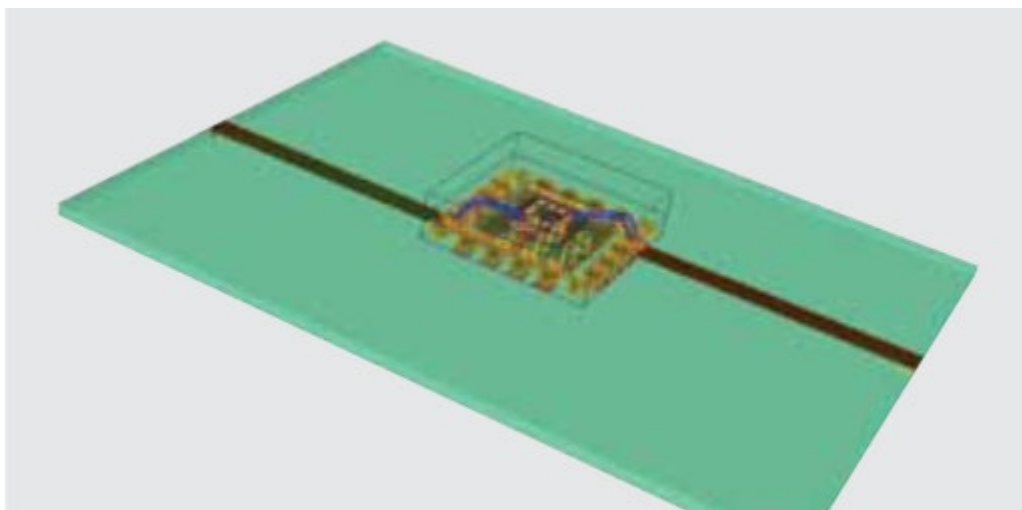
3D-модель досліджуваного QFN-корпусу
